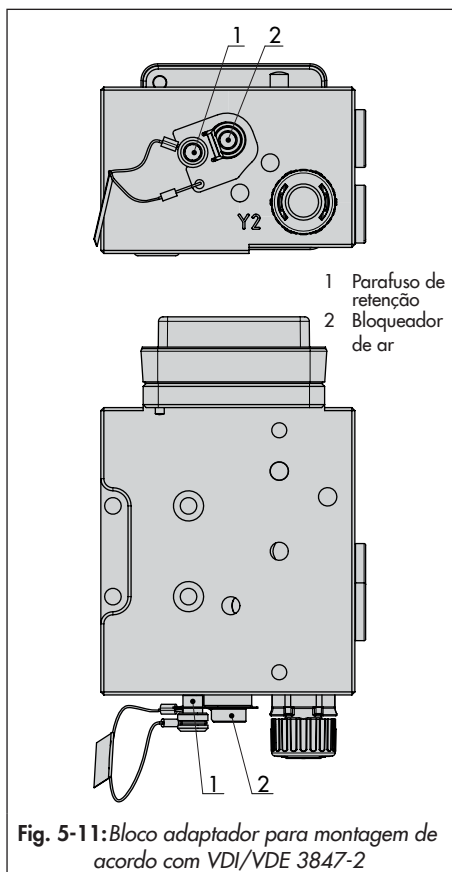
Bloco adaptador para montagem de acordo com VDI/VDE 3847-2
